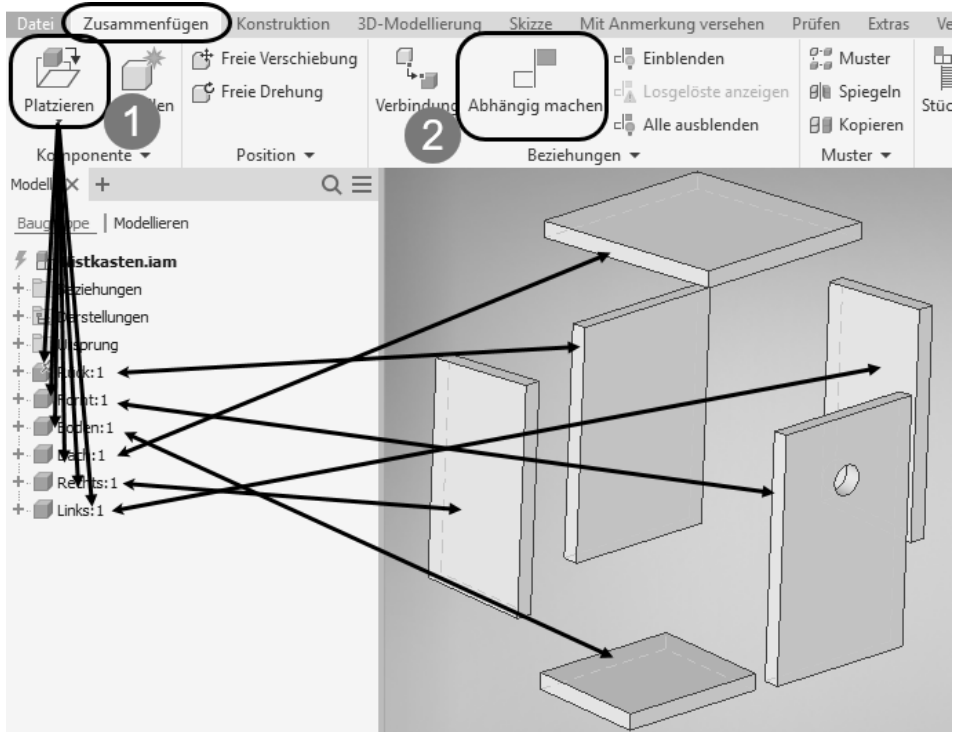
Baugruppe nach dem Bottom-Up-Verfahren zusammenbauen
